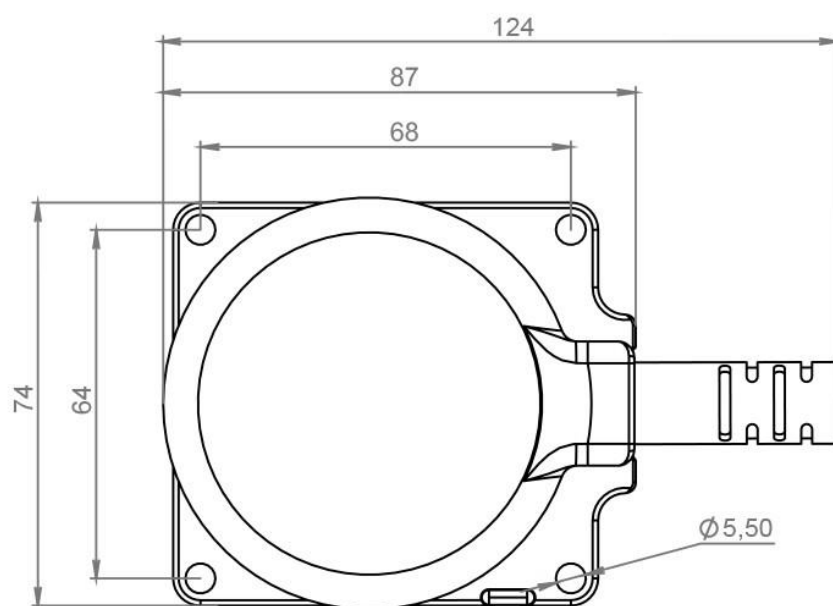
Установочные размеры ДУТ SIENSOR серии D300 – вид сверху
